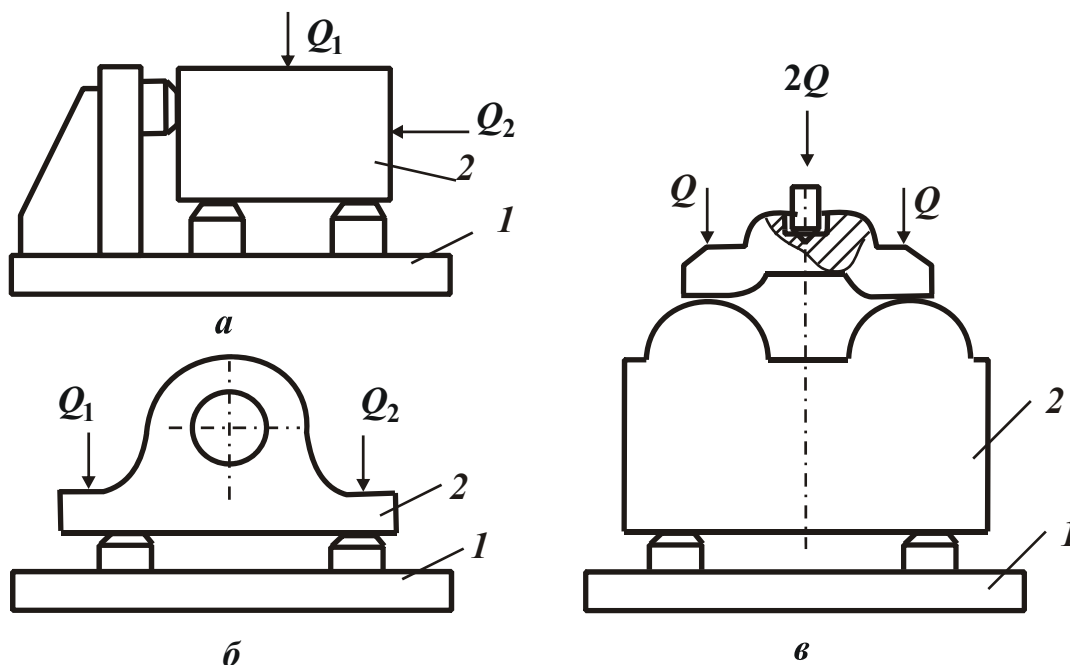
Схемы закрепления заготовки в приспособлении.
